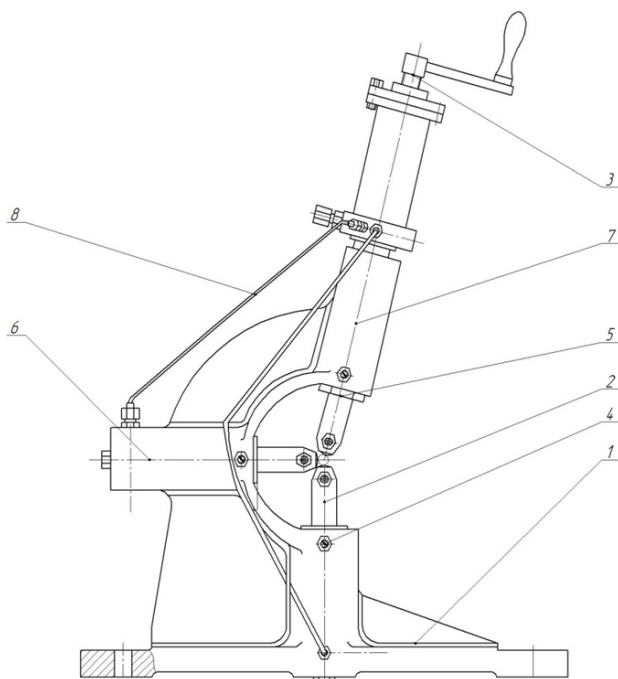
Базовый люнет: 1 – корпус; 2 – опора; 3 – привод зажима; 4 – винт-стопор; 5 – гайка; 6 – гидроцилиндр боковой; 7 – гидроцилиндр вертикальный; 8 – трубопровод
